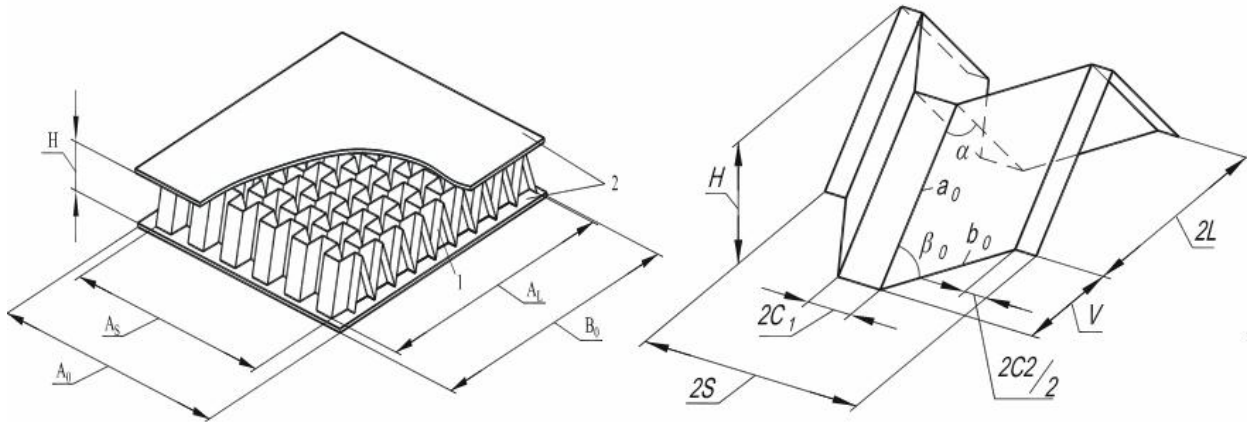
Испытываемый образец: 1 – наполнитель, 2 – обшивки
